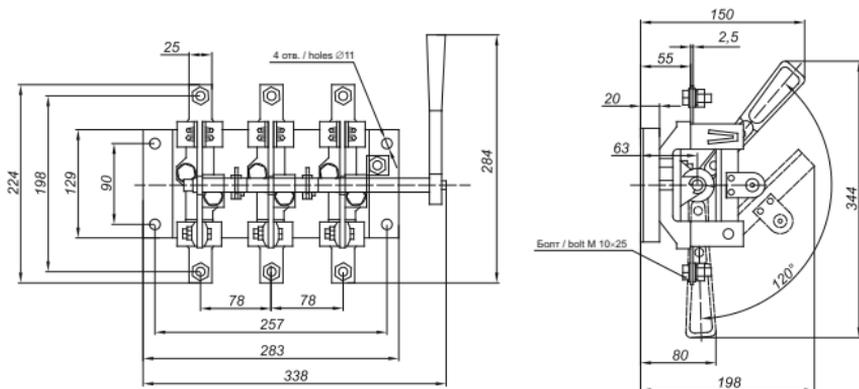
Размеры разъединителей RE19-35-31120 и RE19-37-31120 с боковой рукояткой / Figure 1 – Sizes of disconnectors RE19-35-31120 and RE19-37-31120 with side handle
